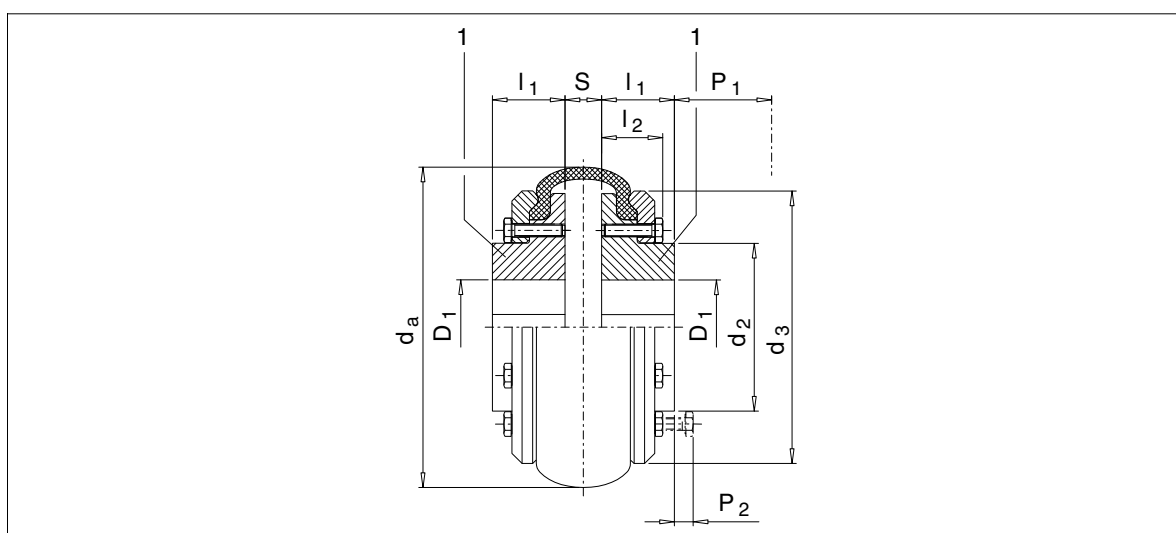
Чертеж с размерами типа EBWN, размер 630
